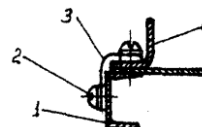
Заземление боковых щитов купе кабины и рамы пола;
